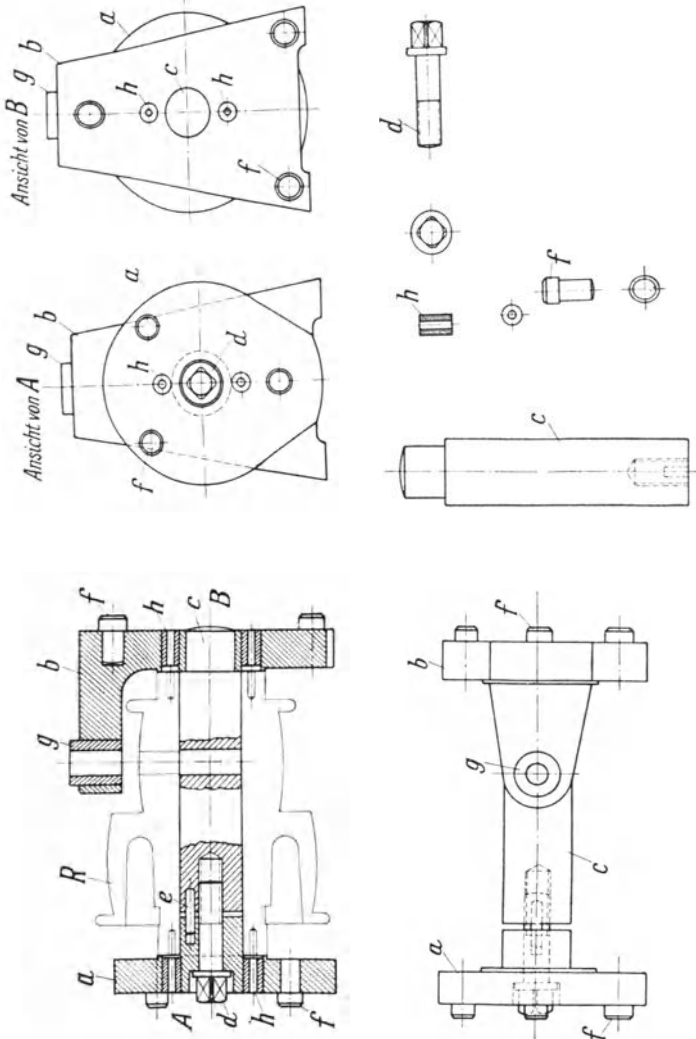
Bohrvorrichtung mit Einzelteile für die Klemmscheibe zur Schleifmaschine Abb. 588.
